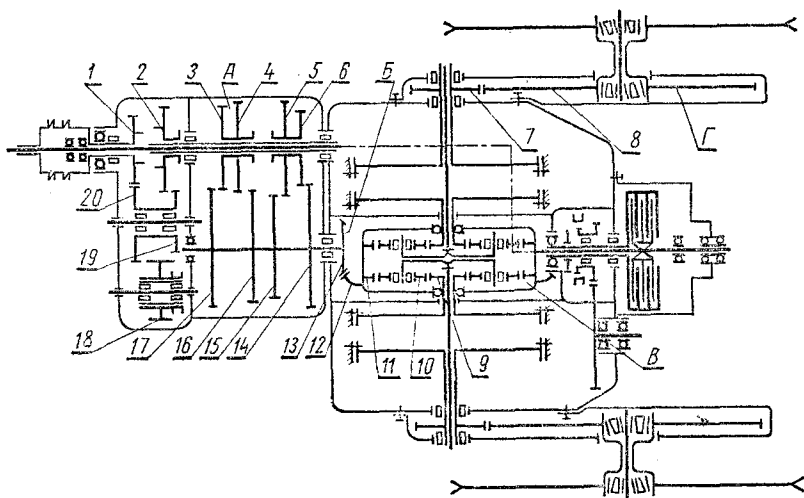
Кинематическая схема механической ступенчатой силовой передачи (трактор Т-4А):
